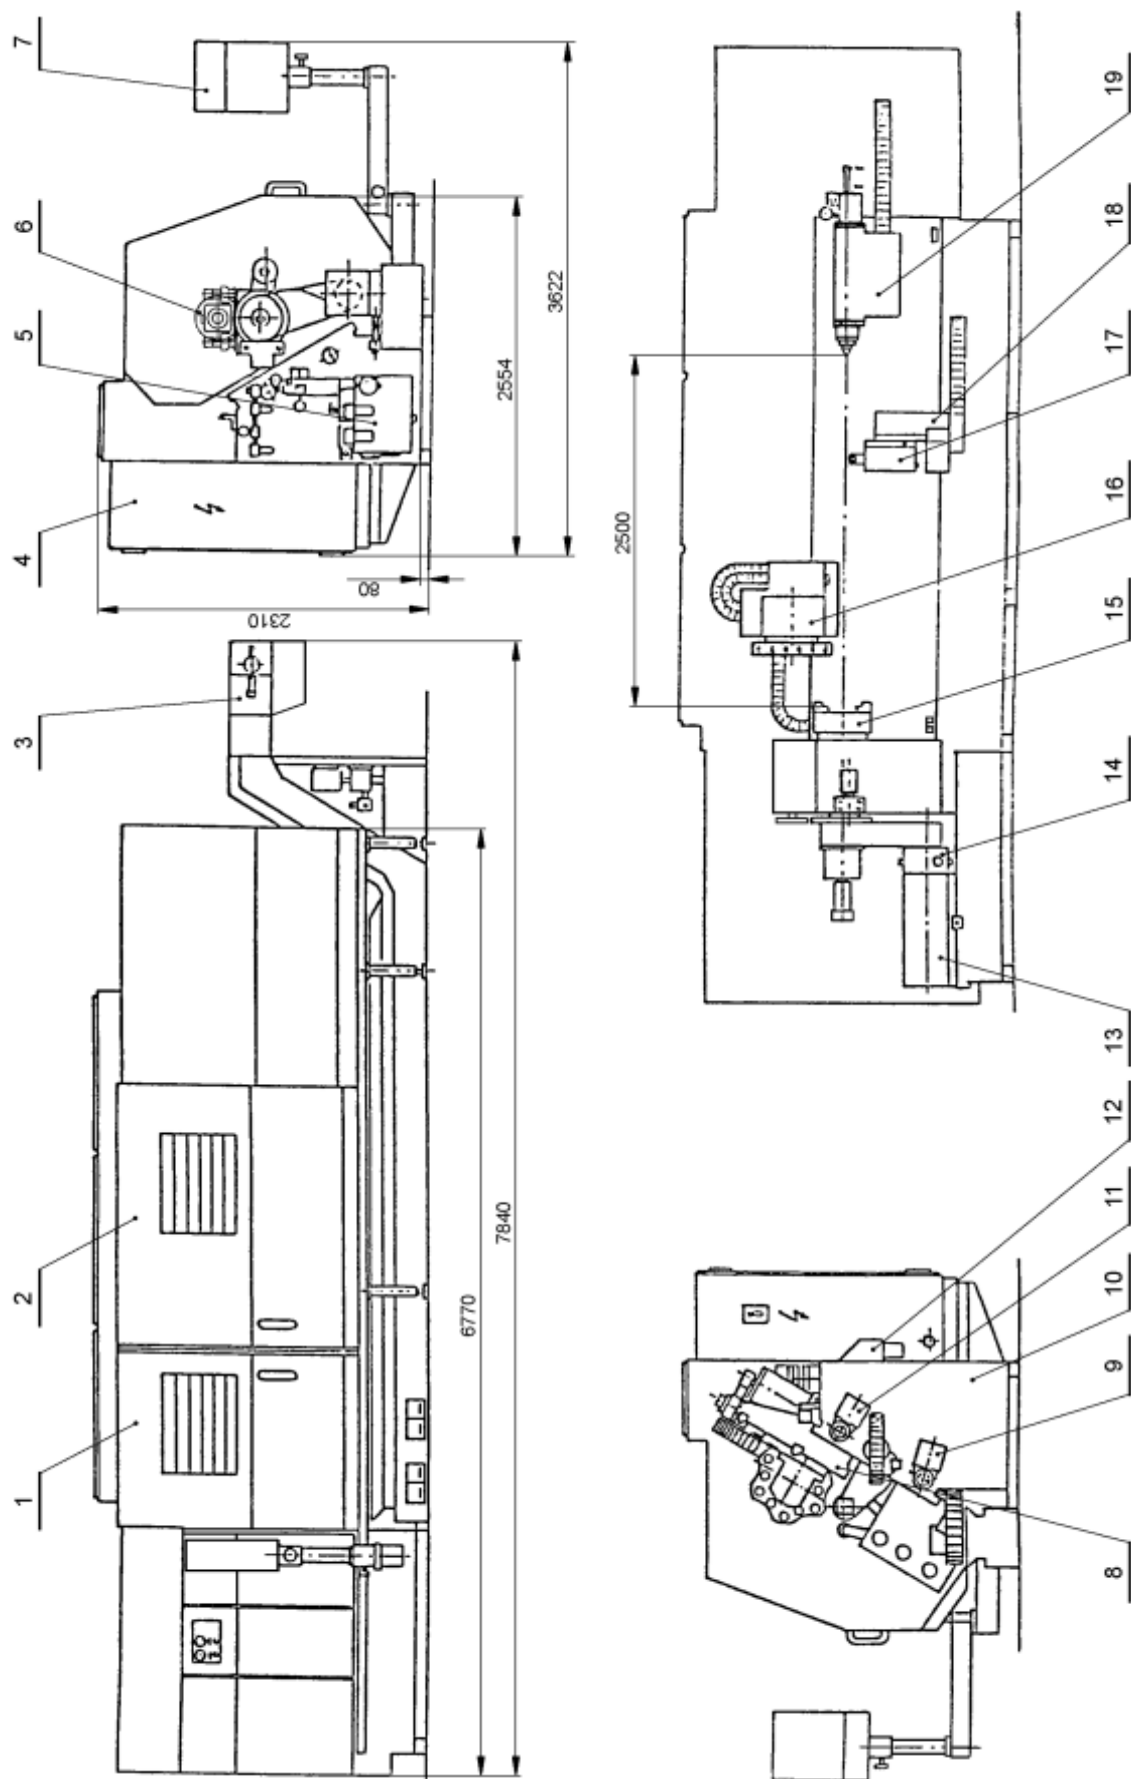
Основні вузли і механізми токарного верстата з ЧПК
